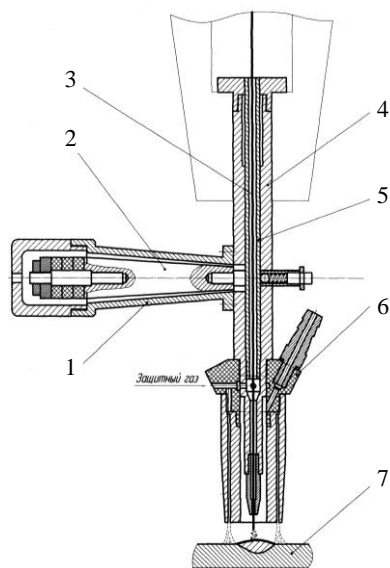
Схема технологической оснастки для наплавки с ультразвуком и металлопорошковой присадкой:
